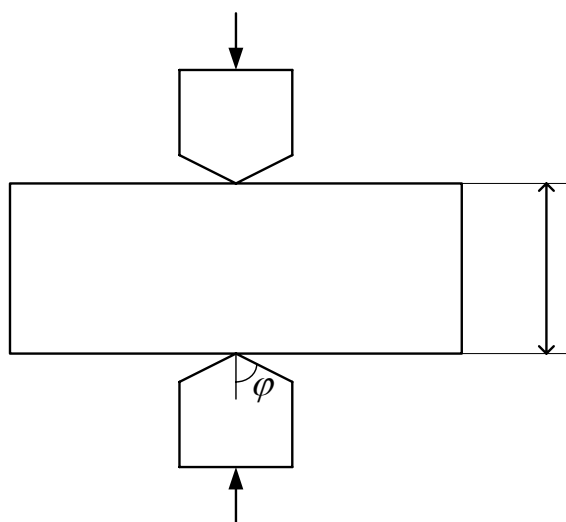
Образец материала, нагруженный симметричным инструментом.
